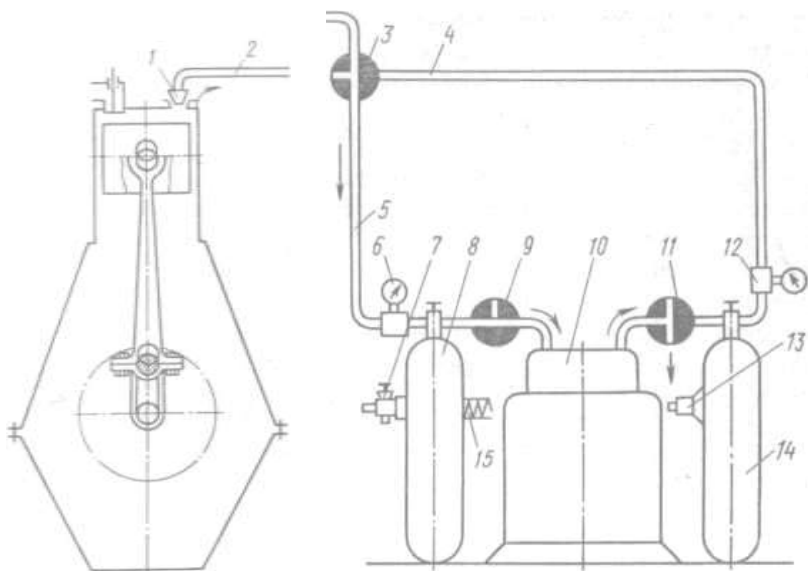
Схема подключения компрессорно-вакуумной установки КИ-13907 к двигателю
